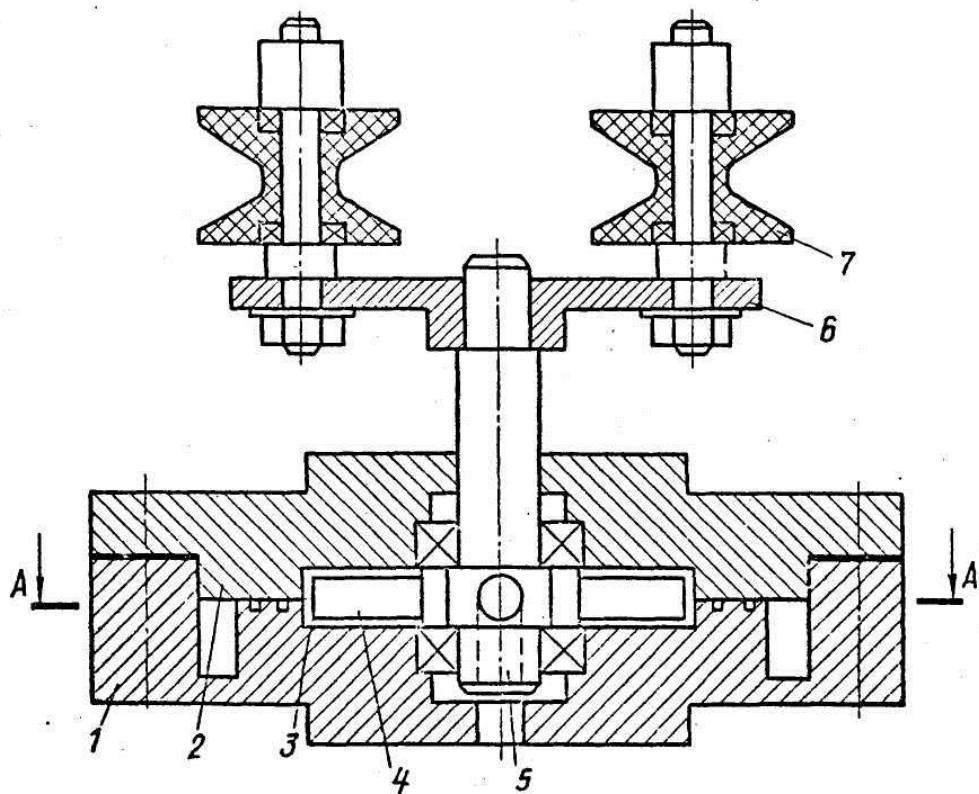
Пристрій для вимірювання натягу рухомої нитки
